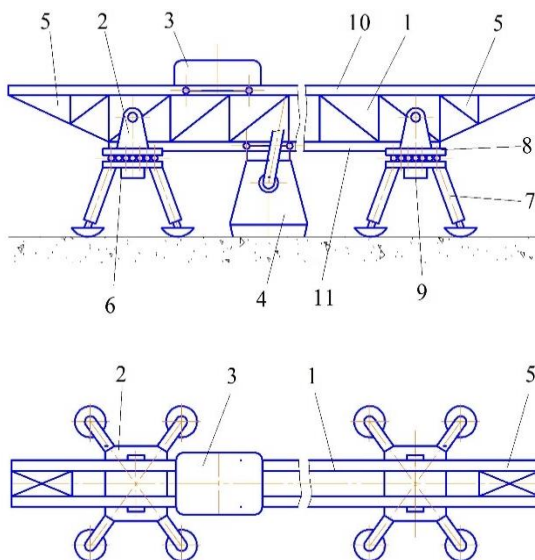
Двухопорная шагающая установка: 1 – ферма; 2 – опора; 3 – противовес; 4 – рабочий орган; 5 – консоль; 6 – опорный стол; 7 – телескопическая штанга; 8 – поворотная платформа; 9 – привод; 10, 11 – направляющие
